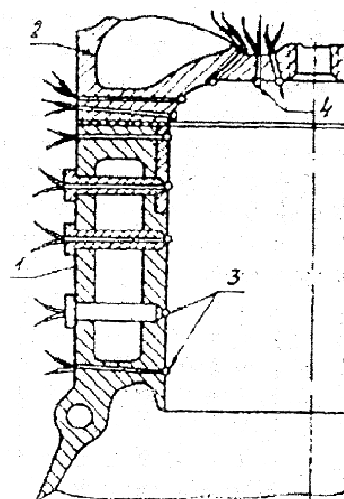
Цилиндр и головка двигателя Р-4, оборудованные термопарами:
